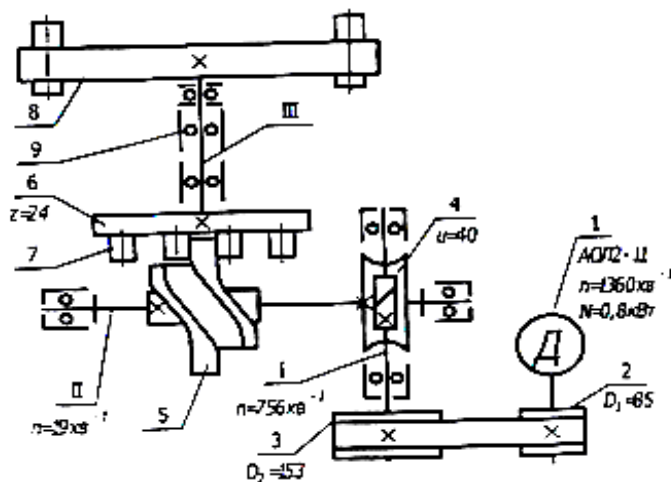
Принципова кінематична схема приводу каруселі багатопозиційної машини з кулачково- роликовим механізмом: 1 – двигун; 2 і 3 – шків пасової передачі; 4 – черв'ячний редуктор; 5 – кулачок-уліта; 6 – роликовий диск; 7 – ролики; 8 – карусель; 9 – підшипниковий вузол
